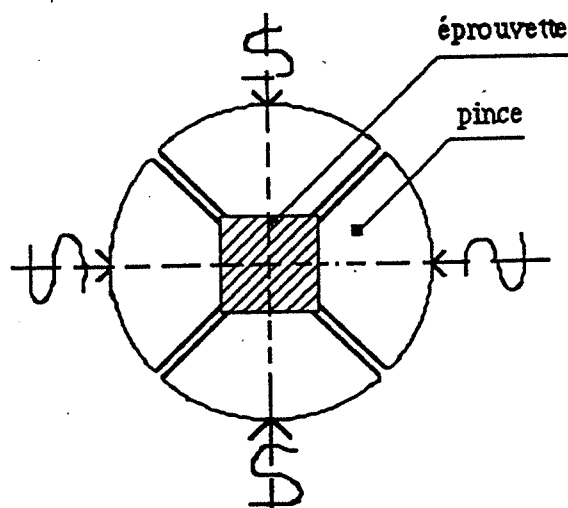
Pince de serrage à quatre pans (voir dessin d'ensemble coupe : B-B).
